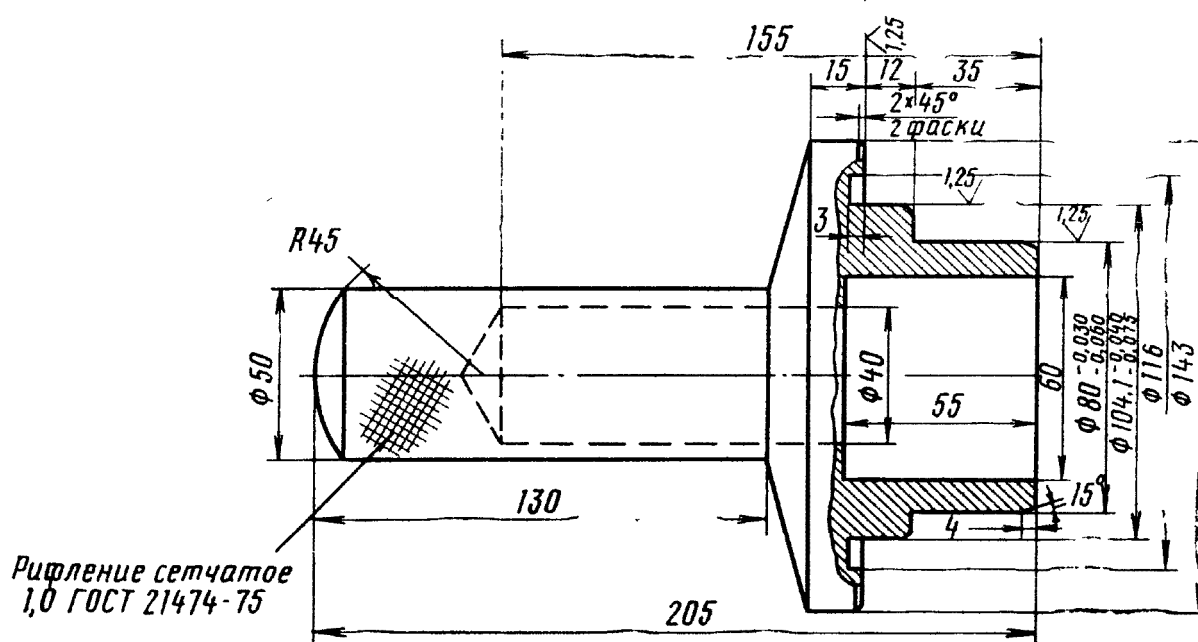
Оправка для запрессовки сальника ступицы колеса
